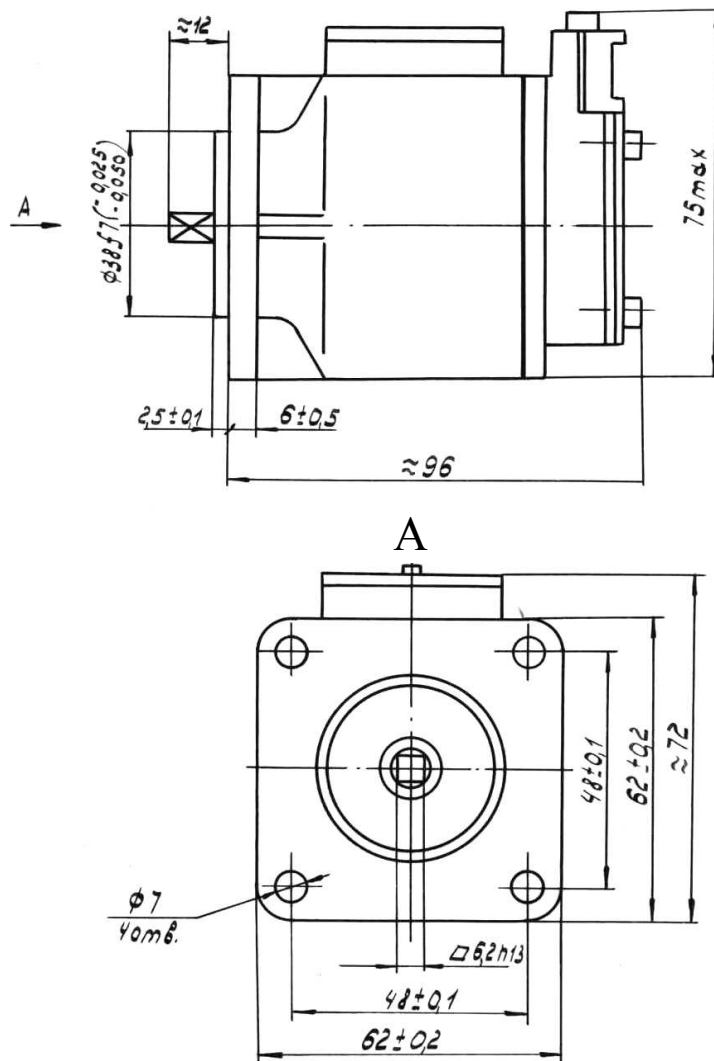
Габаритные размеры первичного преобразователя ППЭ-Д
